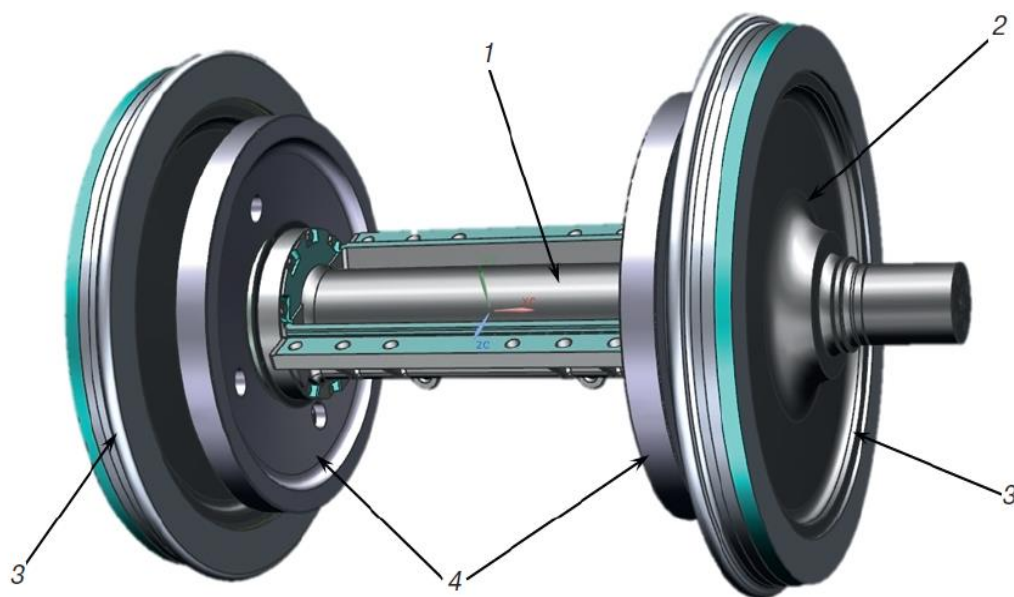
Колесная пара с корпусом моторно-осевых подшипников
